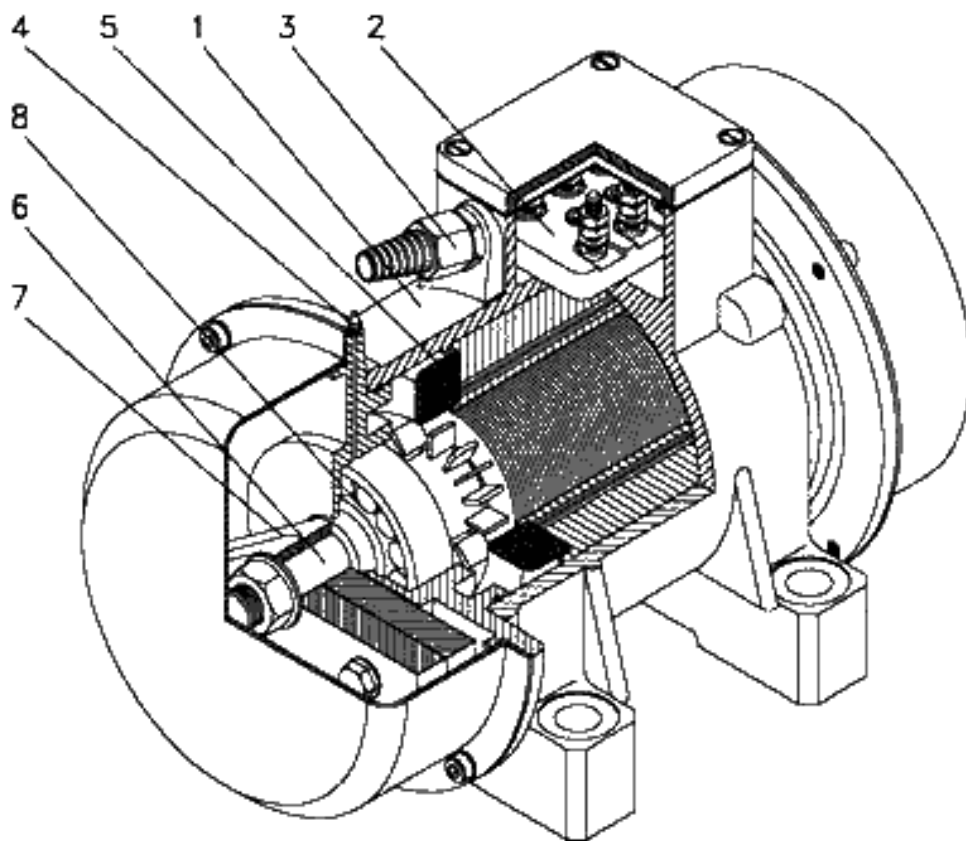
Конструкція вібратора: 1)Корпус вібратора; 2) Клемна коробка; 3)Кабельний сальник; 4)Фланець обойми підшипника; 5)Статор; 6)Вісь ротора; 7)Дебаланс; 8)Підшипник.
